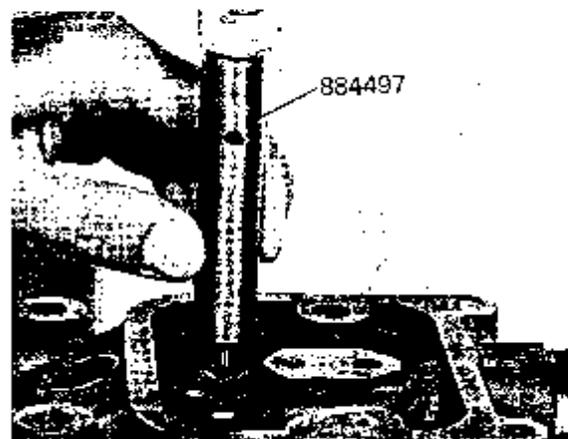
Einbau des Dichtringes für das Einlaßventil
